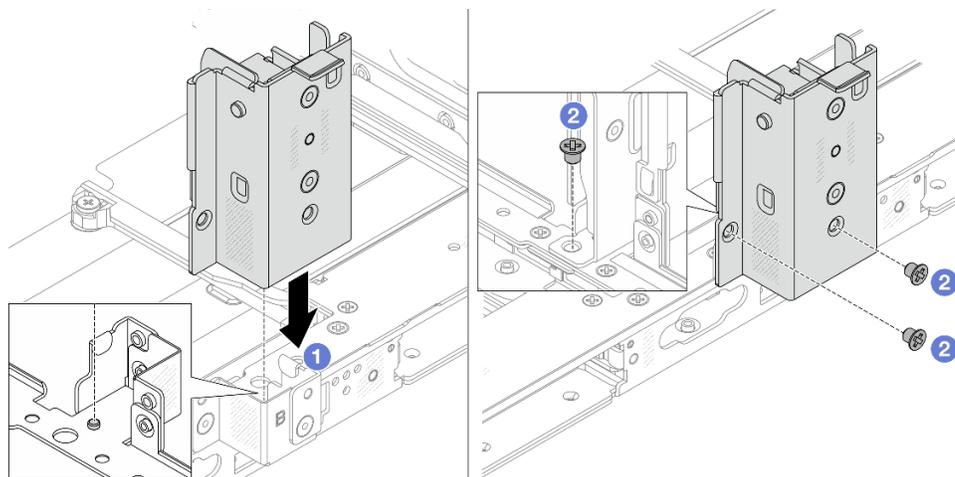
Installazione della staffa posteriore centrale per il montaggio a parete
